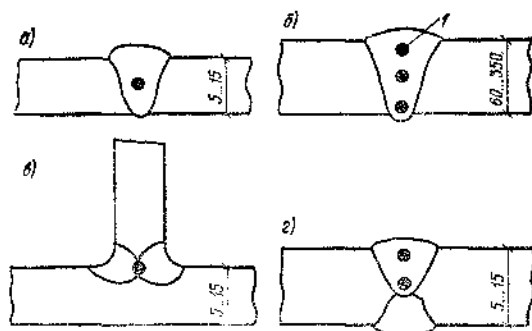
Схема вырезки образцов для испытания металла шва на растяжение при различной толщине основного металла, мм ($q-r$)
